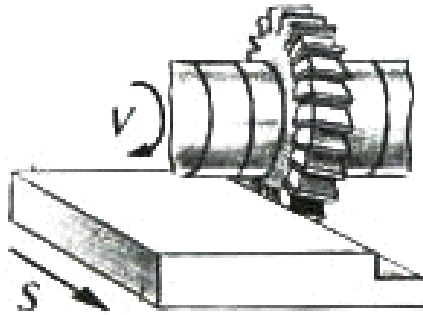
Фрезерование уступов дисковой двусторонней фрезой
